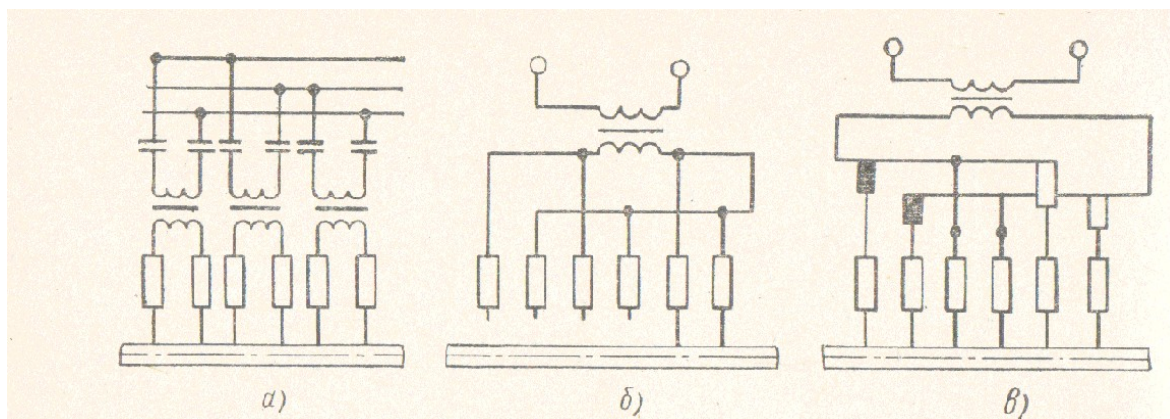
Схемы односторонней многоточечной сварки
